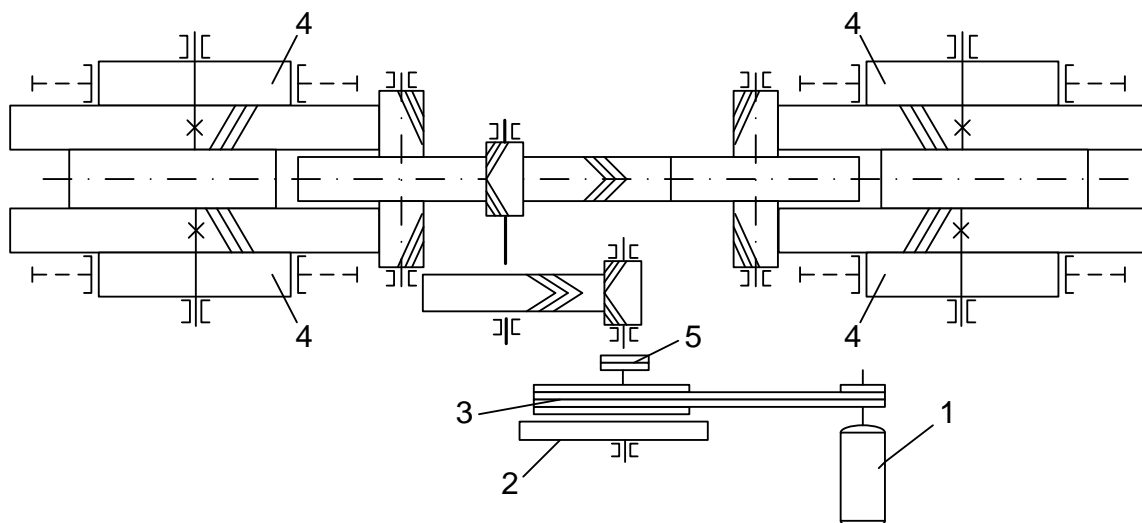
Кинематическая схема передачи механического эксцентрикый пресса: 1 - двигатель; 2 - маховик; 3 - клиноремennая передача; 4 - эксцентрик; 5 – муфта
